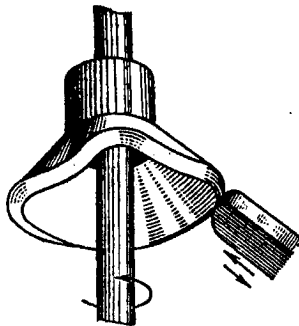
Кулачковий механізм з робочою поверхнею на торці конусного диску
